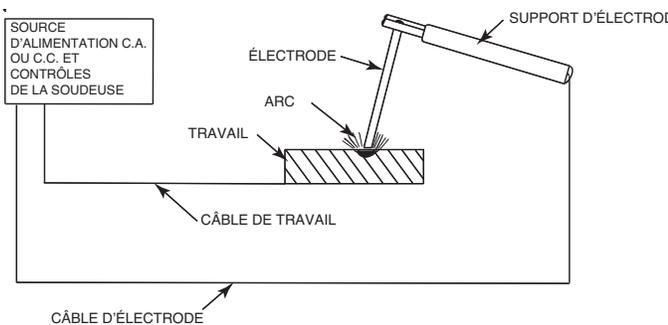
Circuit de Soudage pour Soudage à l'Arc avec Électrode Enrobée (Baguette)
